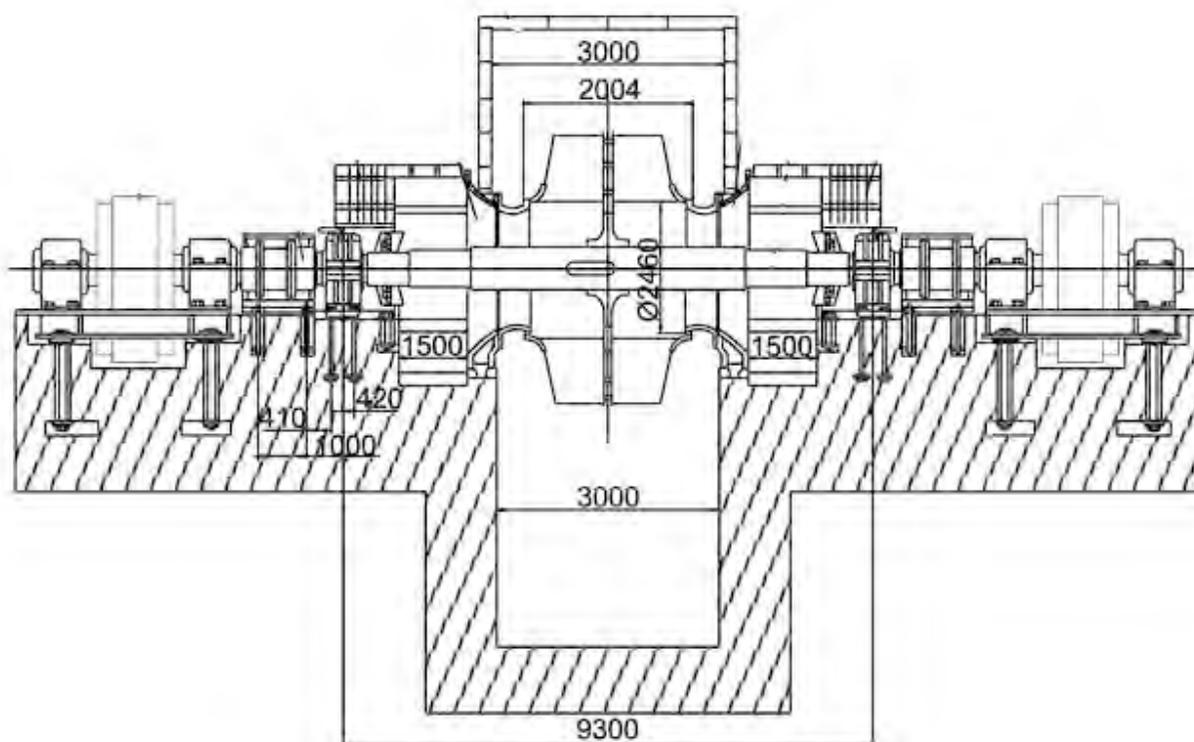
Габаритные и присоединительные размеры вентиляторов ВЦД-47У.
